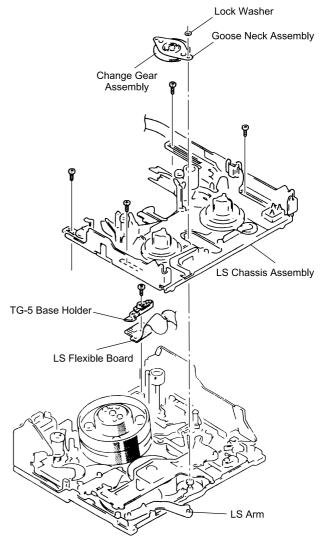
Сборочный чертеж ЛПМ видеокамер Sony (ме-ханизм A)
